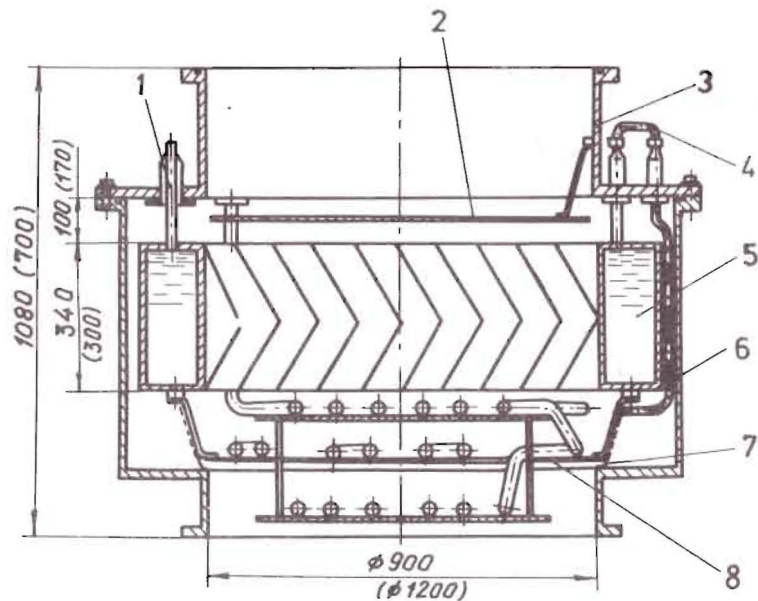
Конструктивная схема азотных ловушек. Без скобок указаны размеры ловушки для агрегата ВА-20, в скобках - для насоса М-4. 1 - подвеска /труба/; 2 - алюминиевый неохлаждаемый экран; 3 - крыша с патрубком вакуумного кожуха; 4 - внешняя переключка линий для паров азота; 5 - бак с жидким азотом и жалюзи; 6 - корпус вакуумного кожуха; 7 - барьер антимиграционный; 8 - экран из меди, охлаждаемый парами азота.
